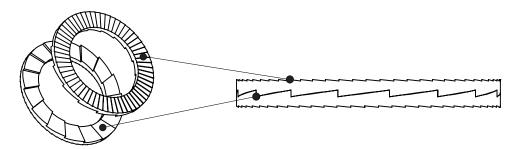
Einbaulage der Nord-Lock® Sicherungsscheiben
